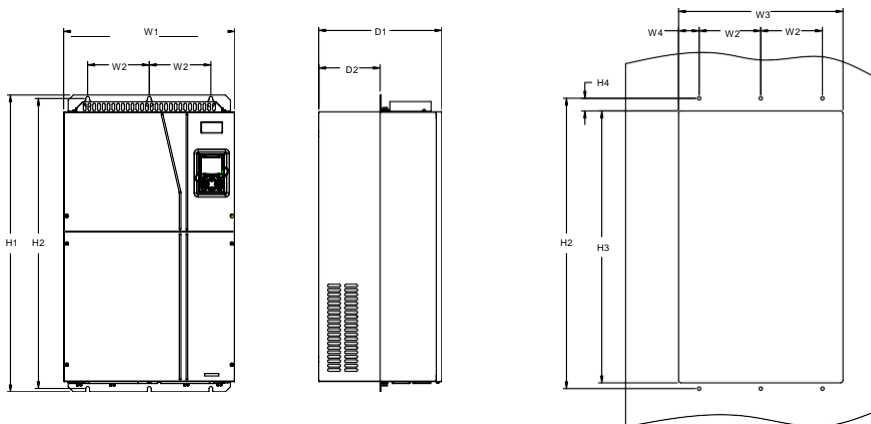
Схема ПЧ фланцевого монтажа 660 В, от 160 кВт до 220 кВт
